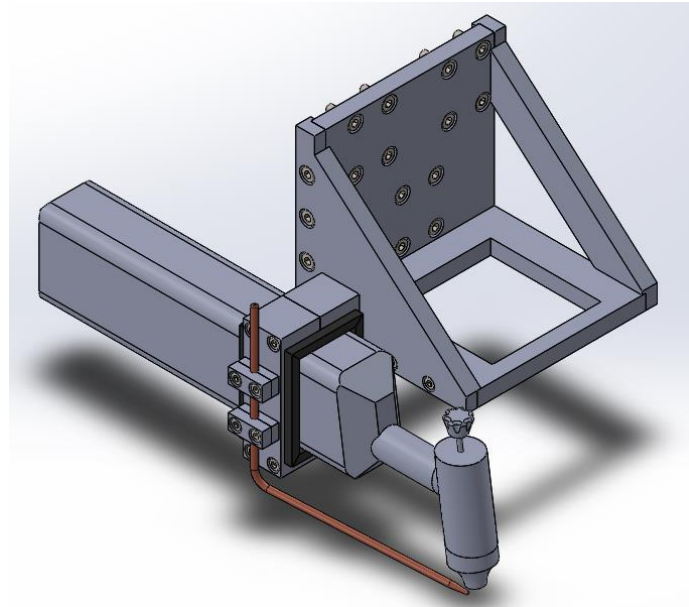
Imagen del diseño CAD del soporte de la antorcha de soldadura GTAW.
